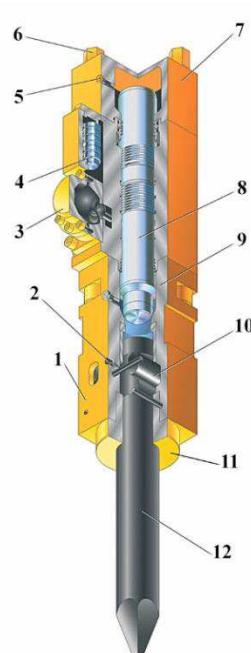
Устройство поршневого гидромолота: 1 – нижний корпус; 2 – масленка; 3 – гидроаккумулятор; 4 – гидрораспределитель; 5 – клапан для заправки азотом; 6 – стяжной болт (шпилька); 7 – крышка цилиндра; 8 – поршень; 9 – рабочий цилиндр; 10 – палец; 11 – нижняя втулка; 12 – рабочий инструмент (пика)
